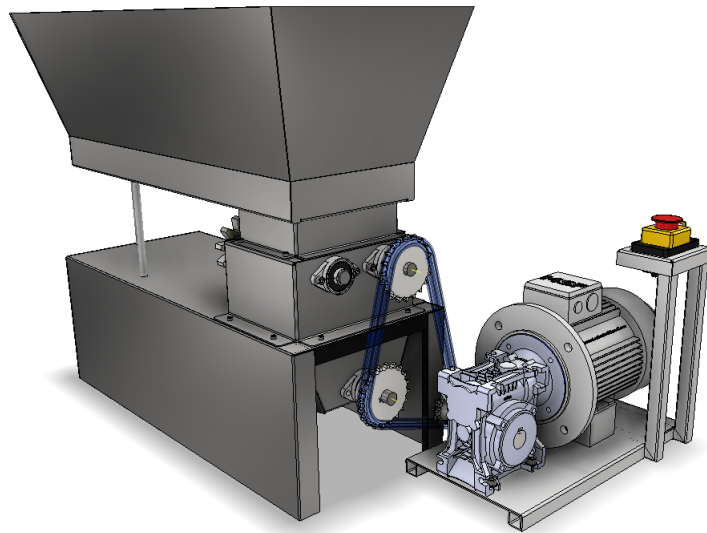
Diseño del Removedor anclado al conjunto motriz
